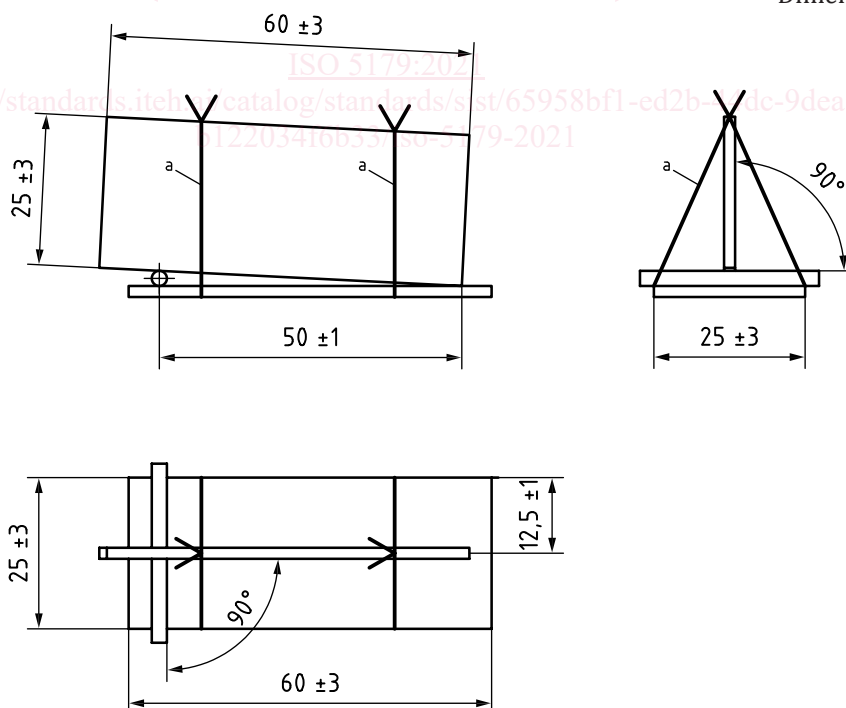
Assemblage de l'éprouvette pour assemblages en T, fil de maintien avec $\varphi = 0,8$
